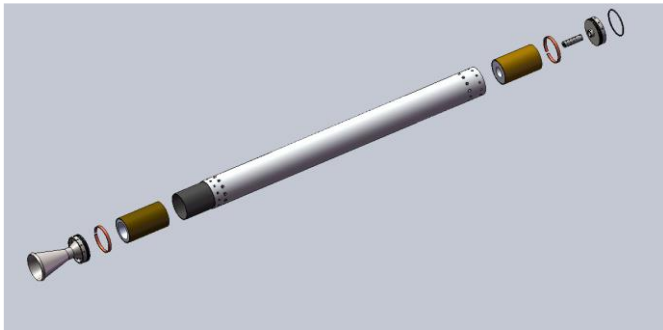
Vista explosionada del motor cohete y sus principales componentes.
